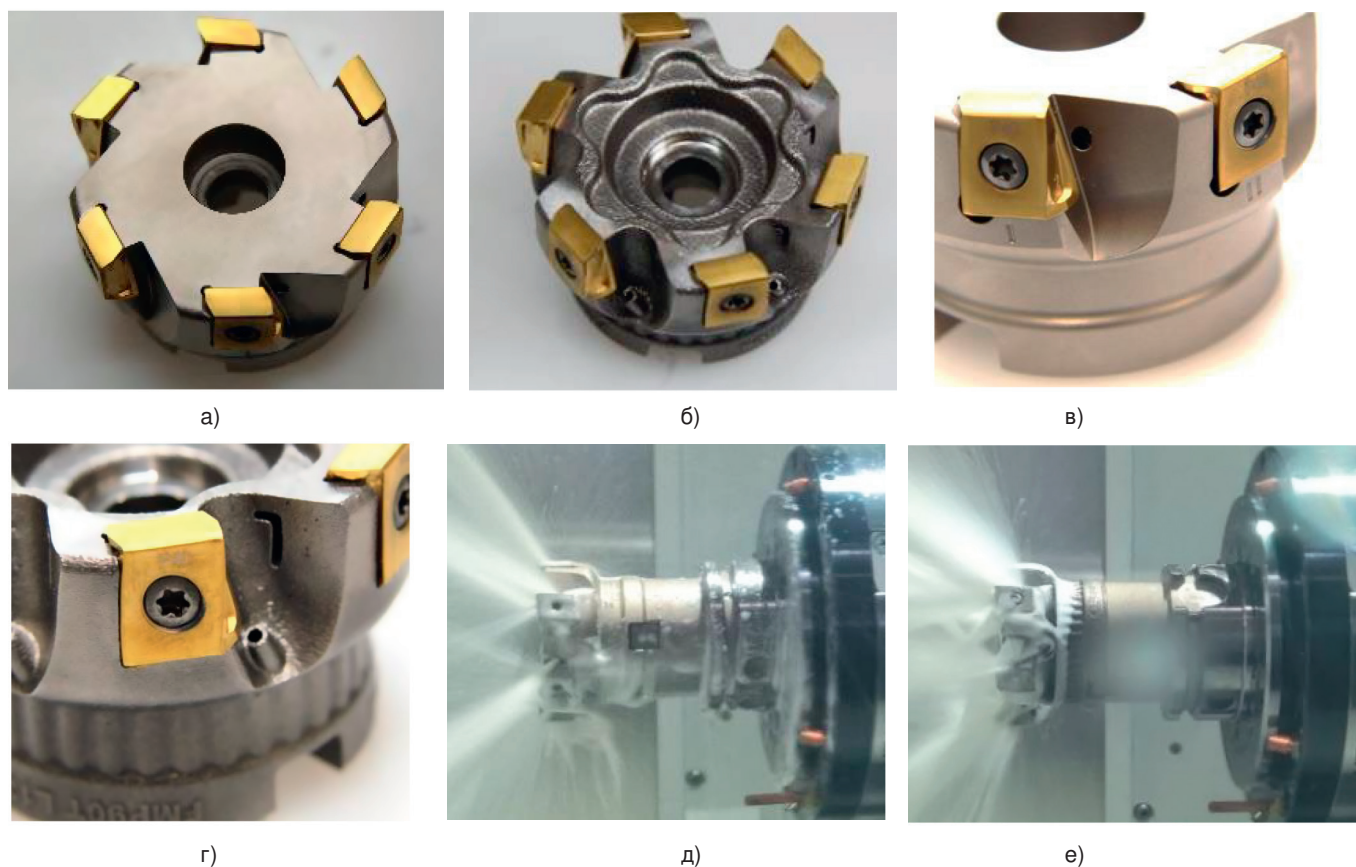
Корпус фрезы, изготовленный по традиционной (а, в, д) и аддитивной (б, г, е) технологии
